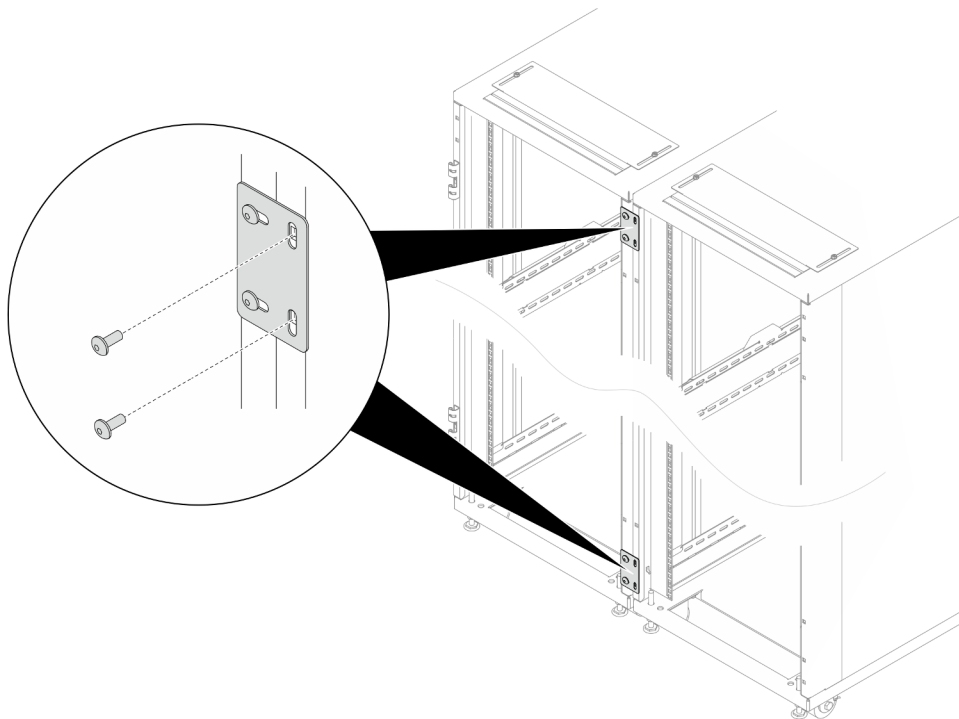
Rimozione delle viti per preparare l'installazione dell'estensione
